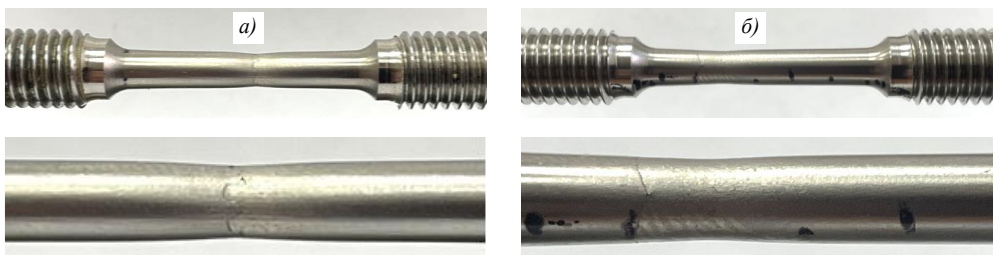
Внешний вид типичного (*a*) и аномального (*б*) разрушения образцов
